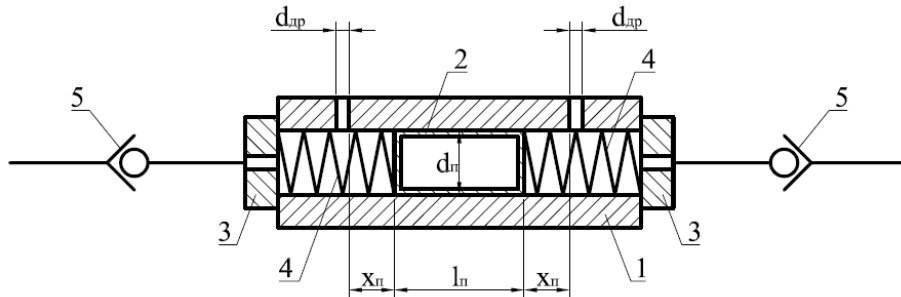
Расчетная схема демпфирующего устройства в гидроприводе механизма подъема стрелы. 1 — корпус; 2 — плунжер; 3 — крышка; 4 — пружина; 5 — обратный клапан.
